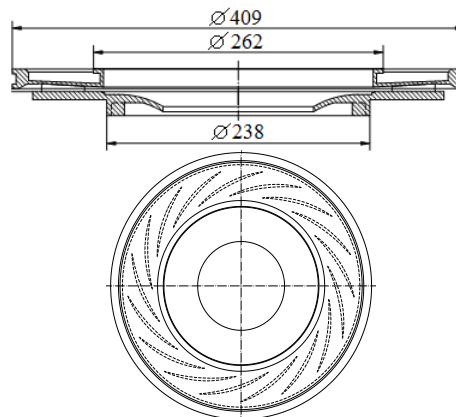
Эскиз прототипа опытной сварной конструкции
